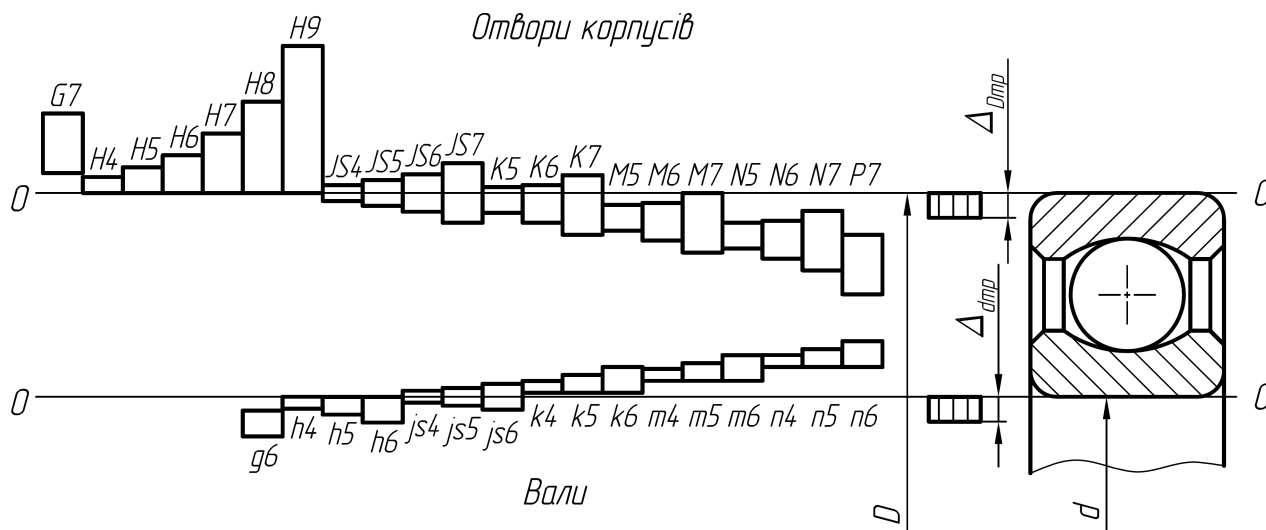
Схема розташування полів допусків для посадок підшипників на вали і в отворах корпусів
